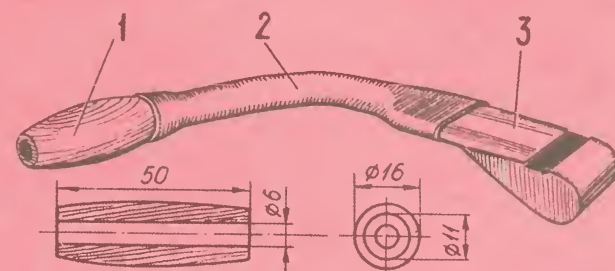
Звуковой индикатор: 1 — деревянная пробка; 2 — соединительный шланг; 3 — свисток.
